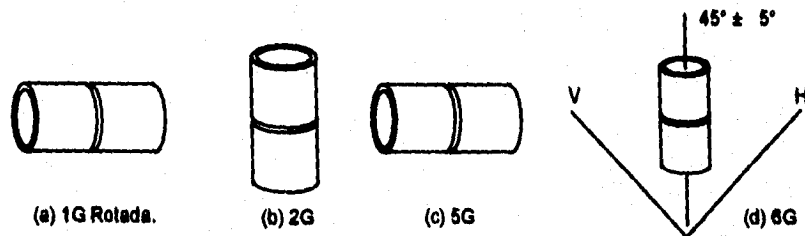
QW- 461.4 Posiciones de prueba, para soldaduras de ranura en tubería.
